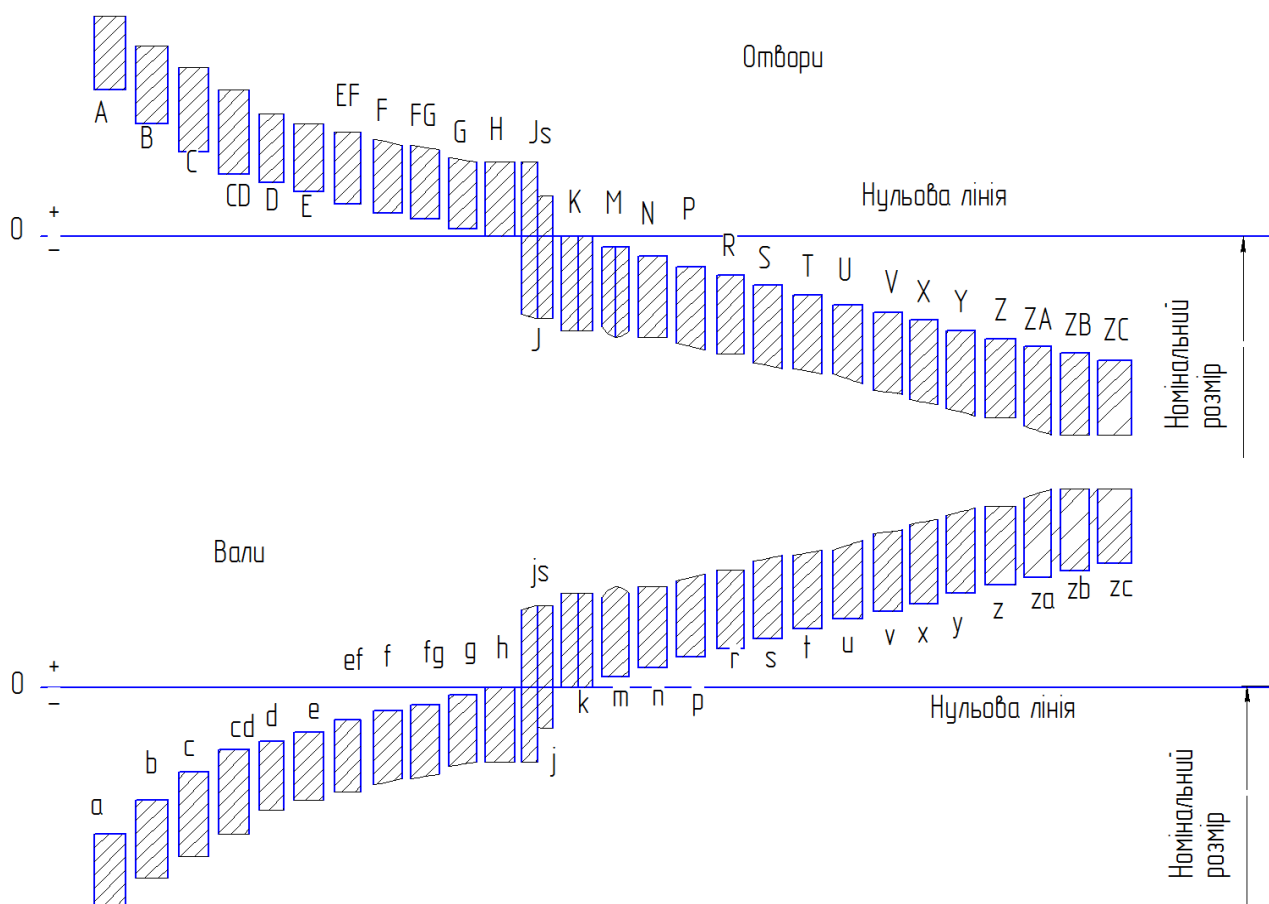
Схема розташування полів допусків з різними основними відхилами
